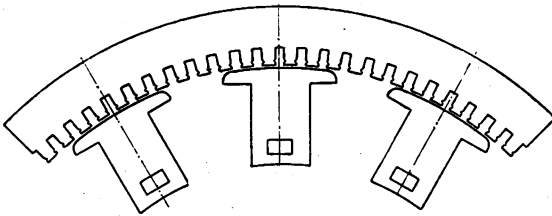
Blechschnitt einer Wechselstrommaschine.
